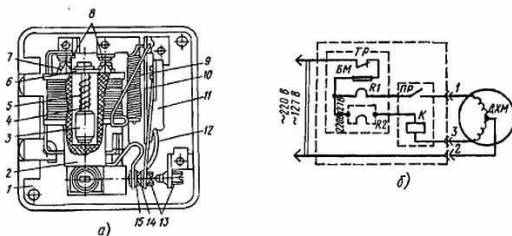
Пускозащитное реле РТК-Х: а — конструкция: 1 — корпус реле; 2 — корпус катушки; 3 — сердечник; 4 — стержень сердечника; 5 — наружный сердечник; 6 — планка; 7 — подвижные контакты пускового реле; 8 — неподвижные контакты пускового реле; 9 — нагреватель; 10 — металлическая пластина; 11 — упор; 12 — контактодержатель; 13 — регулировочные винты; 14 — подвижный контакт защитного реле; 15 — неподвижный контакт защитного реле; б — электрическая схема: ДХМ — электродвигатель холодильника; БМ — биметаллическая пластина; R1, R2 — нагреватели; К — катушка; ТР — тепловое реле; ПР — пусковое реле
